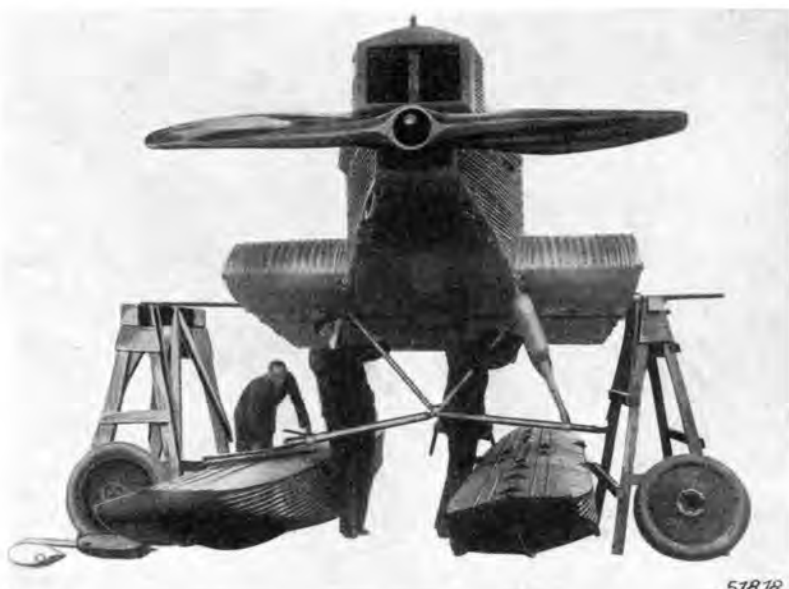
Die Laufräder einer Junkers-Maschine werden gegen Schwimmer ausgetauscht.
